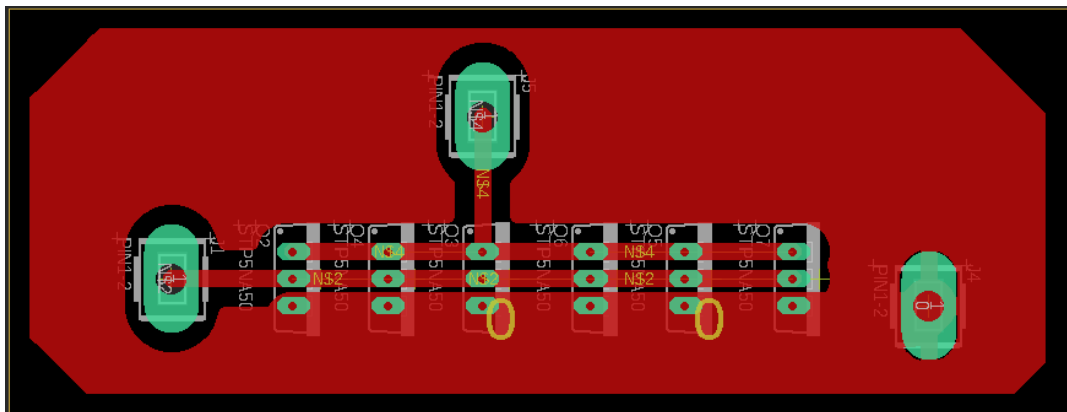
PCB Diseñada para realizar la función de interruptor "LS"
